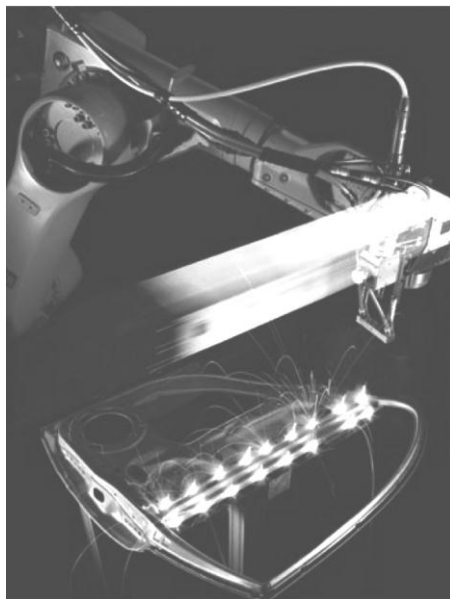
Laserstrahlschweißen einer Automobiltür mit einer Laserscanneroptik [85]
